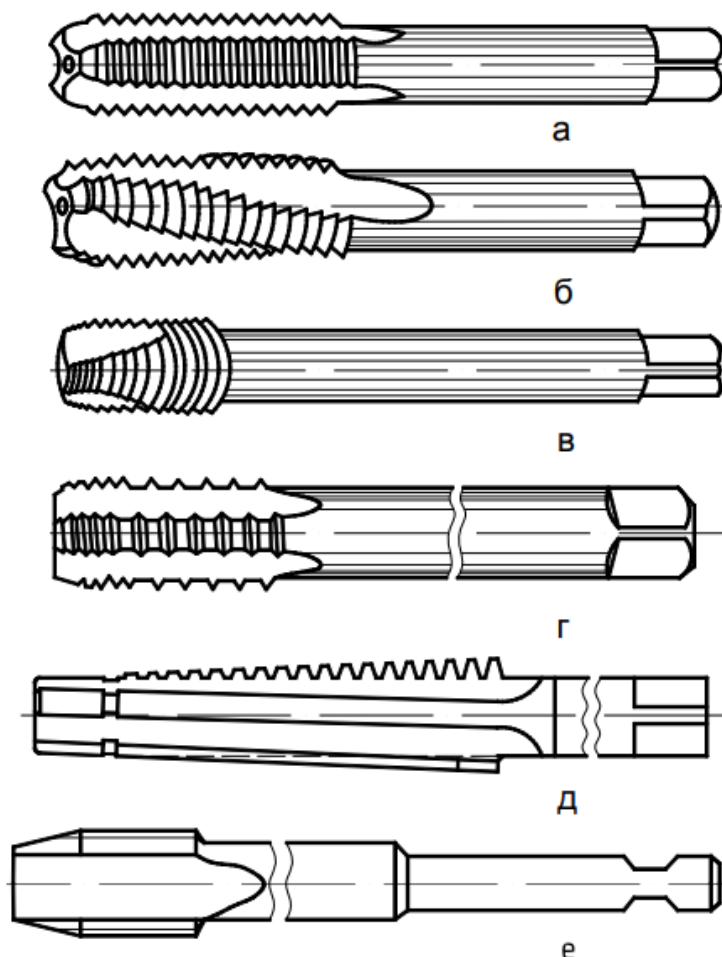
Типы метчиков: а, б, в – с прямыми, винтовыми и укороченными стружечными канавками; г – с шахматным расположением зубьев; д – с скорректированным профилем зубьев; е – гаечные метчики
